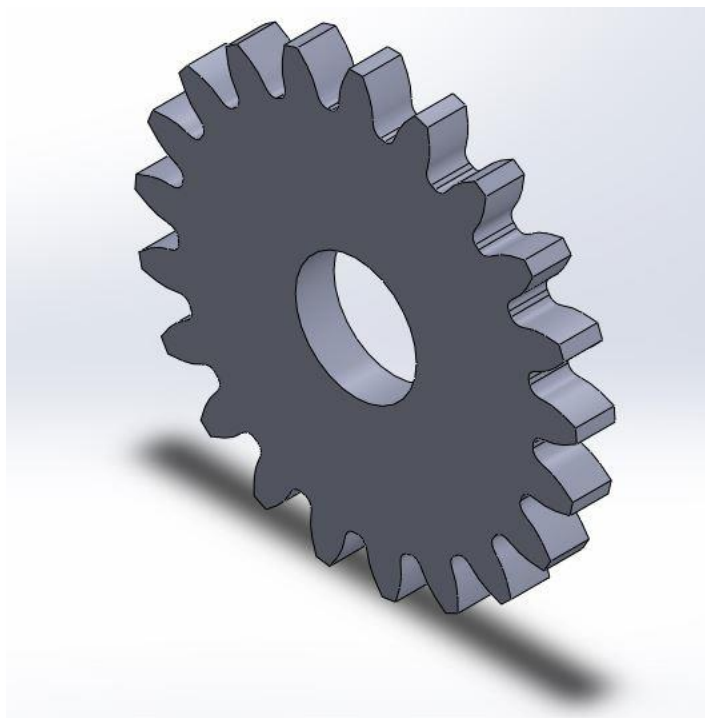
Engrenagem completa com 21 dentes, módulo de 5mm e ângulo de pressão de 20°
